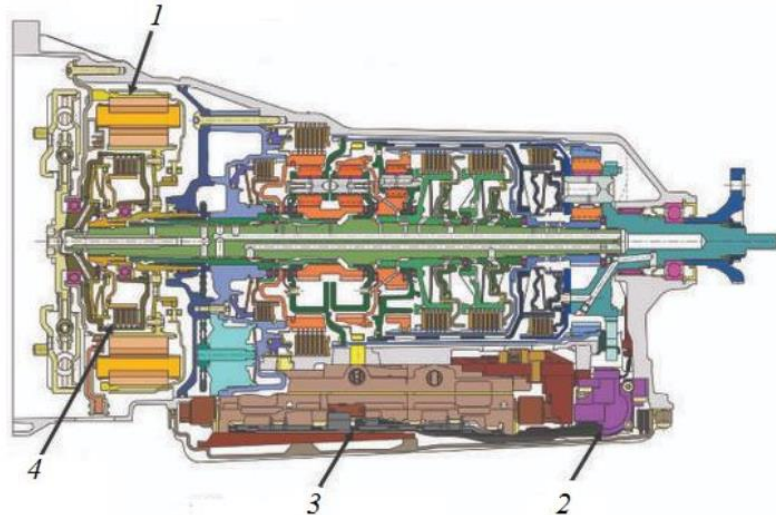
Поперечний перетин коробки передач 8HP70, версія «повний гібрид»:
